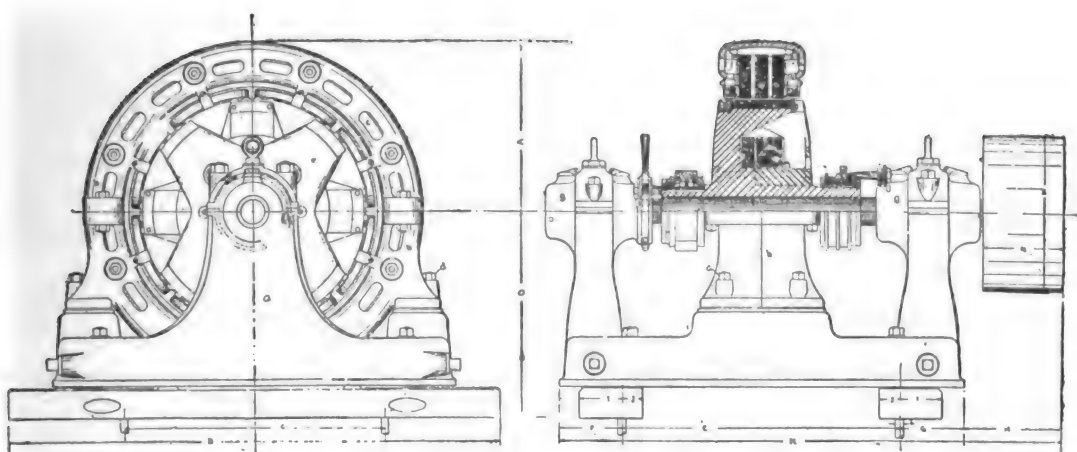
Elévation et coupe de l'alternateur Walker conduit par courroie.
